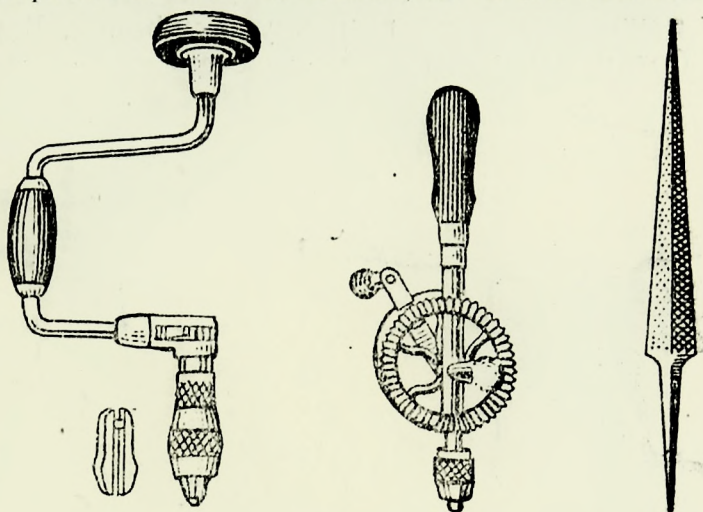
Ручной коловорот и сверла для сверления дыр в стекле
